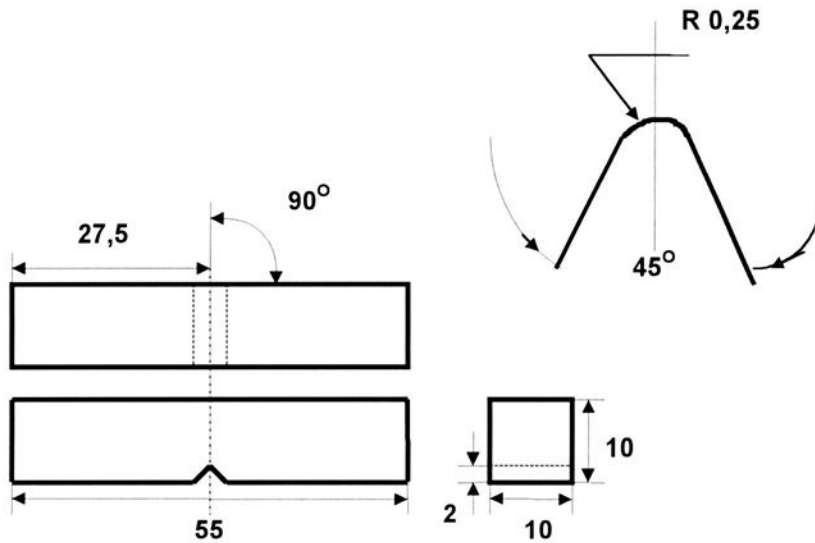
Corpo de prova de impacto conforme norma ASTM E23⁴⁴.
